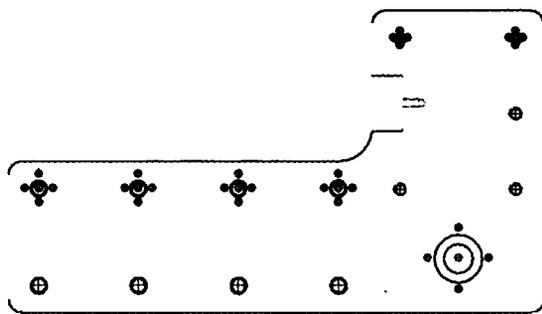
Выбор элементов чертежного вида на размещения набора ординат
